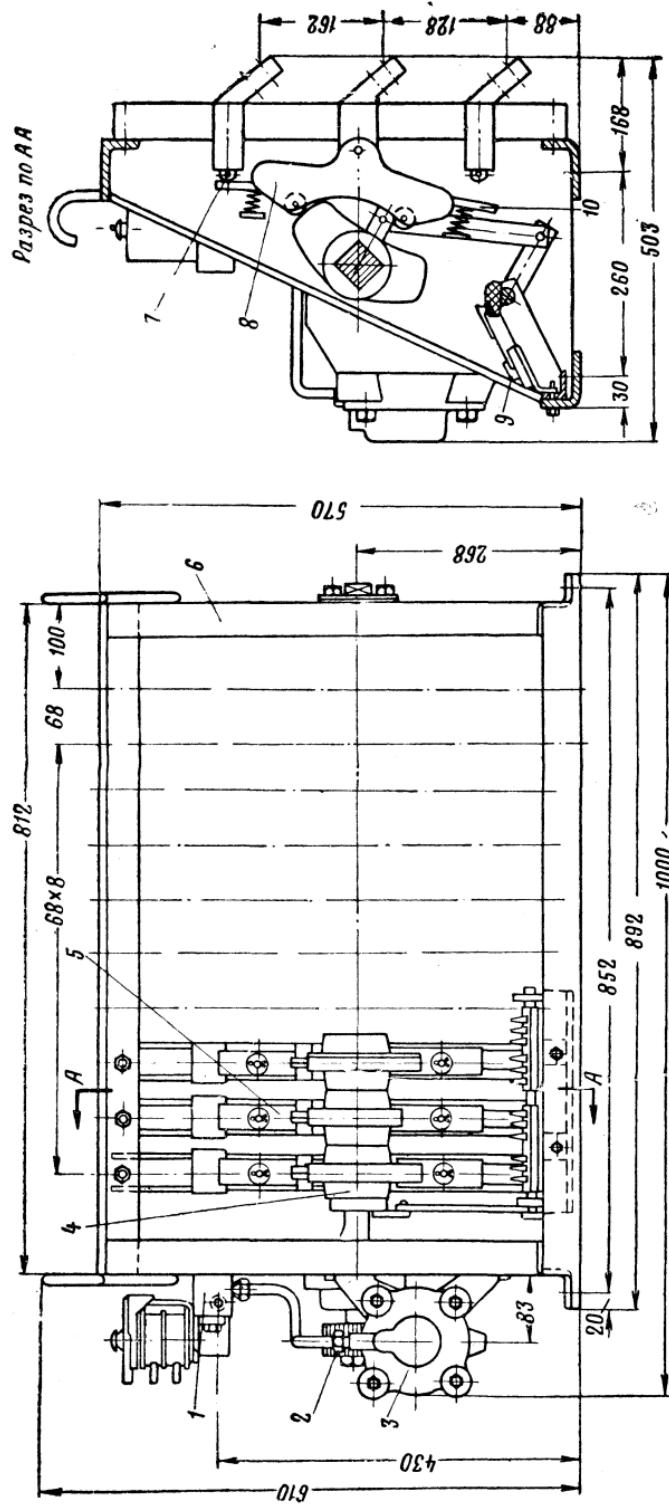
Реверсор РК-8 и тормозной переключатель ТК-8:
